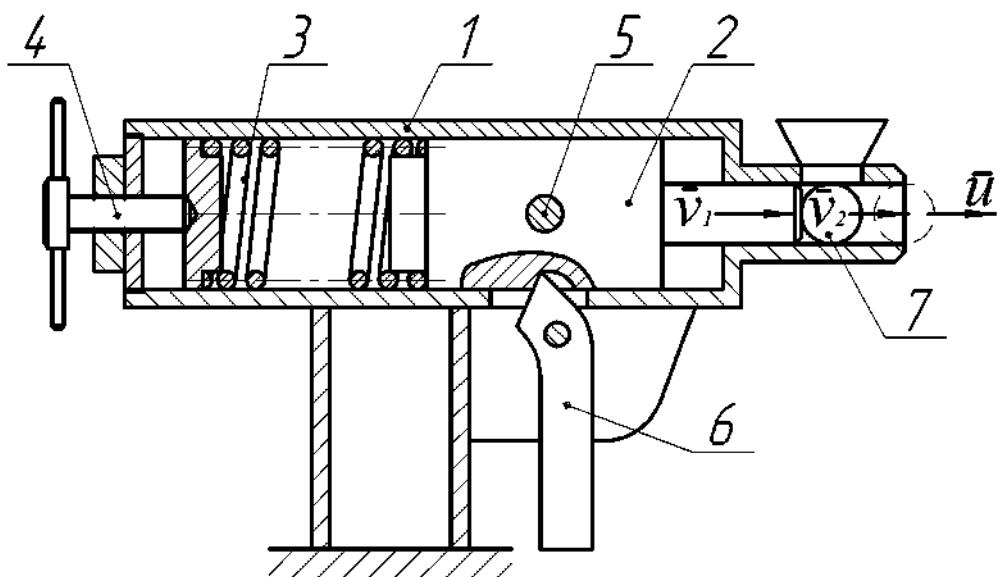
Схема устройства для проведения обработки единичного зерна сои ударной нагрузкой: 1 – корпус; 2 – плунжерный выталкиватель; 3 – рабочая пружина; 4 – винт регулировки степени сжатия рабочей пружины; 5 – элемент устройства взвода; 6 – стопорное устройство; 7 – зерно сои.
